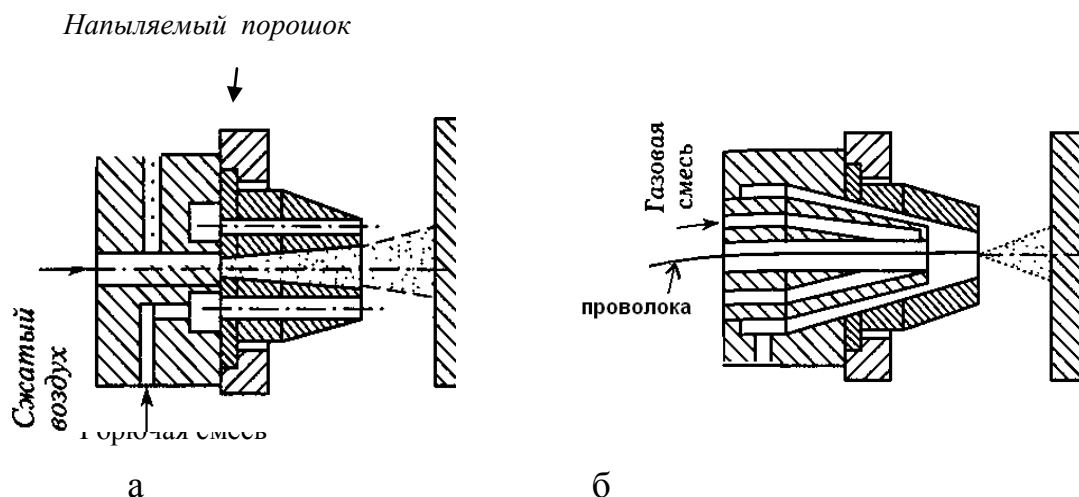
Схема процессов газопламенного напыления с виде порошков и проволоки
